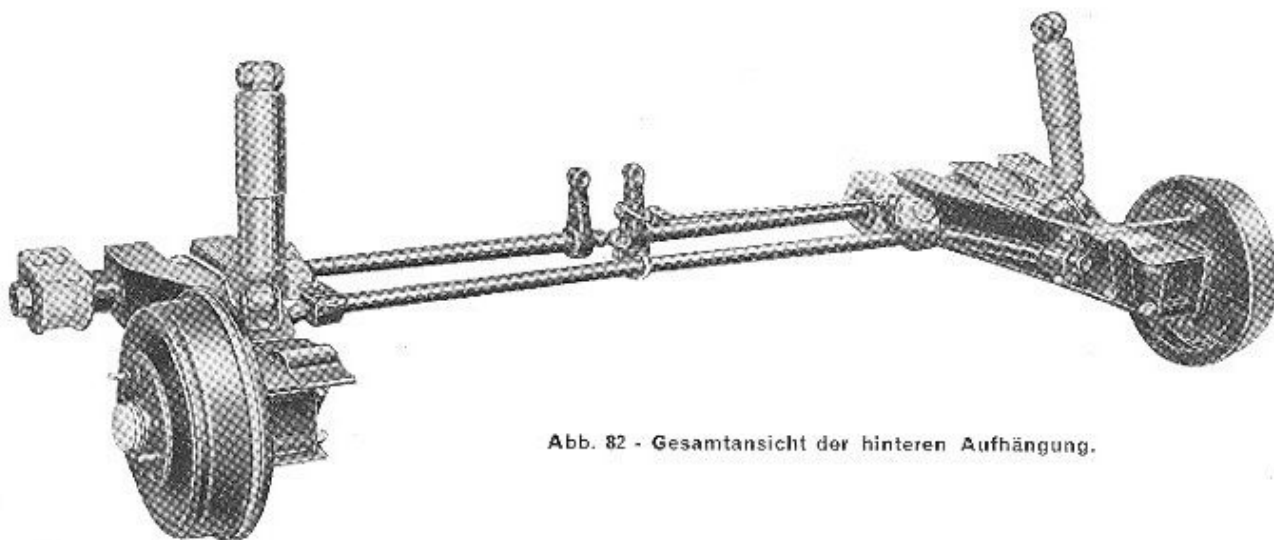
Gesamtansicht der hinteren Aufhängung.
